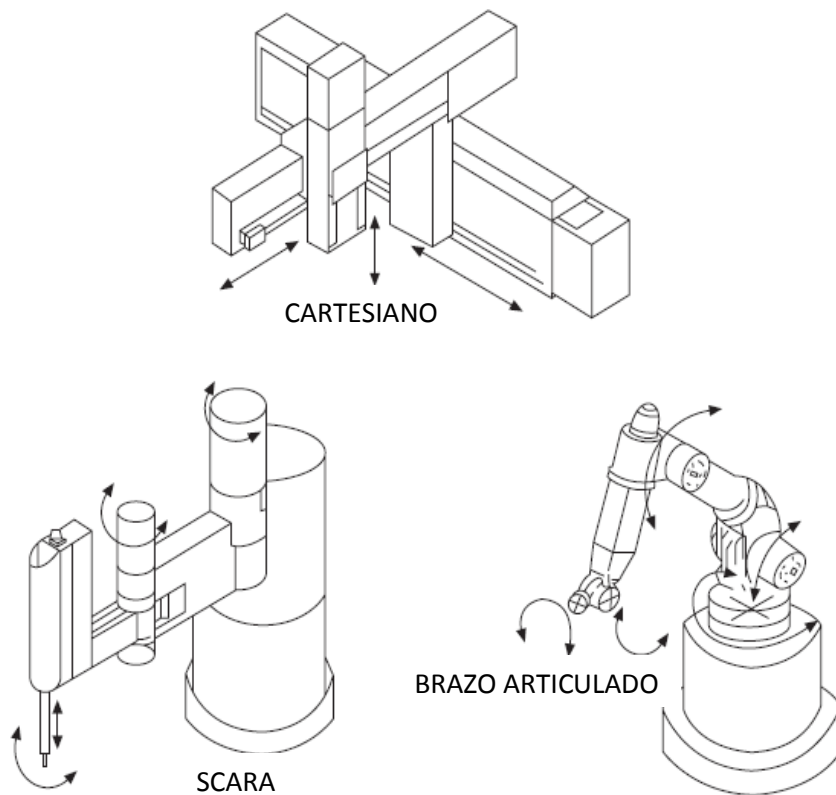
Configuraciones típicas de Robots soldadores.
